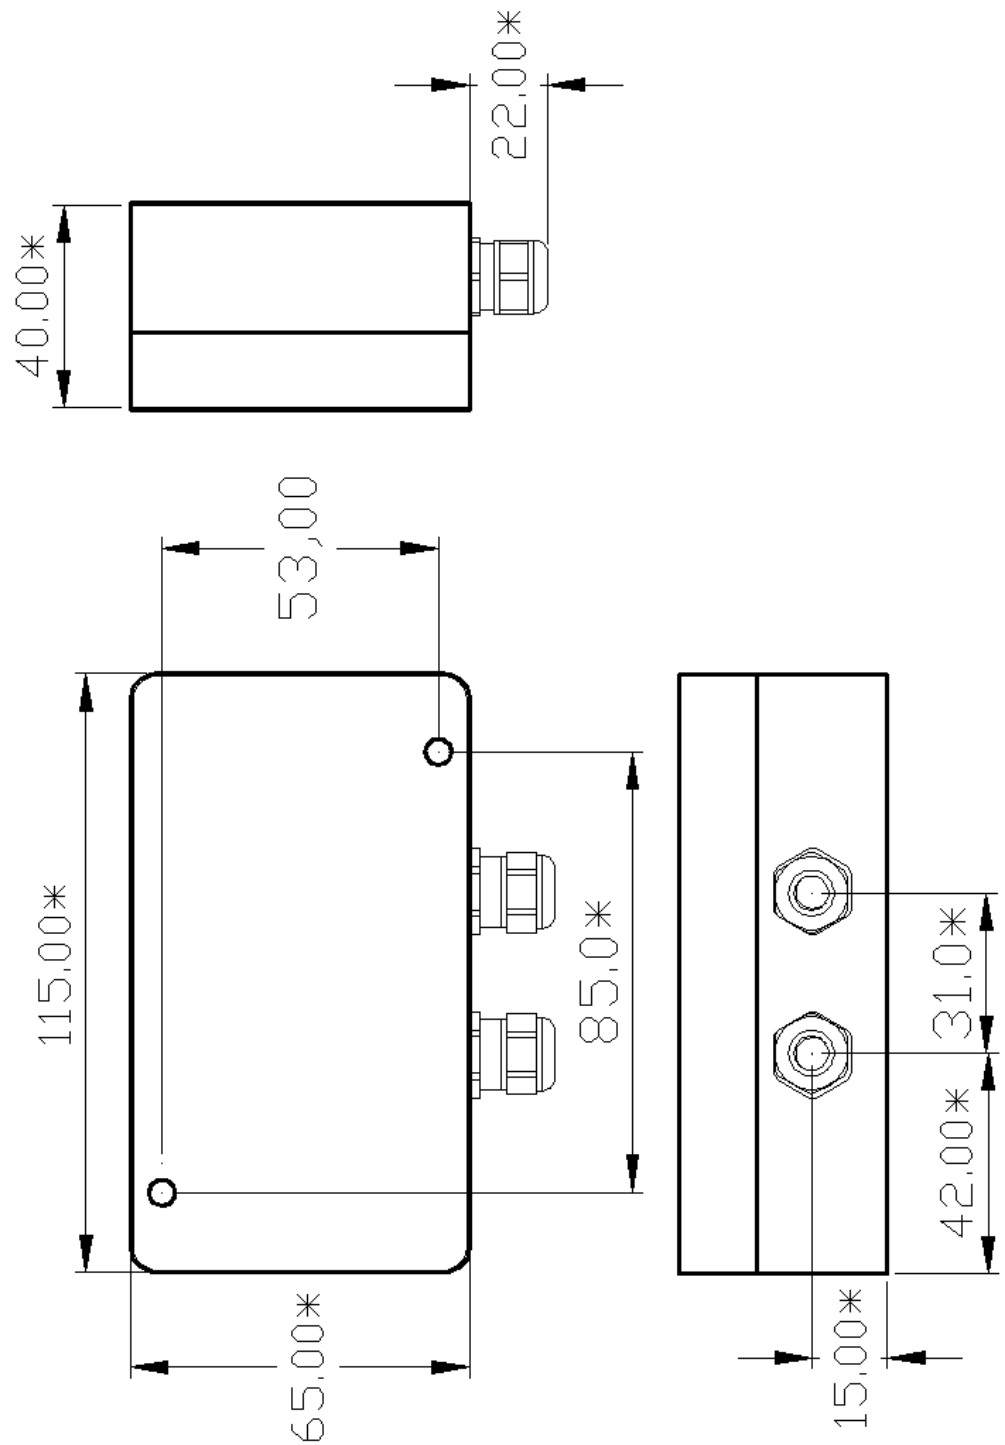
Габаритные размеры корпуса контроллера (размеры приведены для справки).
